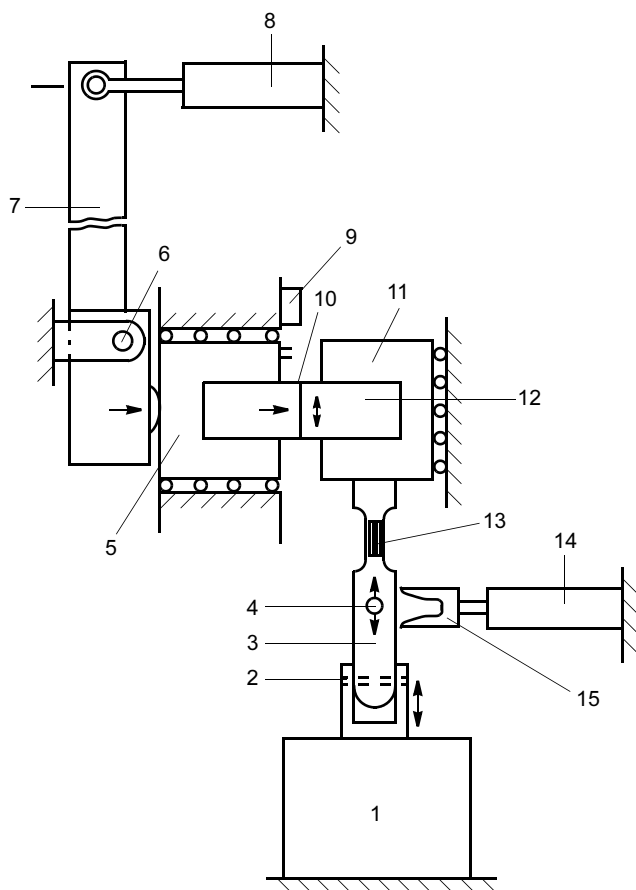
Схема экспериментальной установки для СЛТ [9]: 1 — генератор для испытания на усталость; 2 — штифт; 3 — тяга; 4 — установочный штифт; 5 — фиксатор (неподвижный); 6 — ось поворота; 7 — плечо рычага; 8 — пневматический узел для передачи фрикционного и ковочного давления; 9 — выключатель (предохранитель); 10 — стык; 11 — фиксатор (колеблющийся); 12 — стыкуемые образцы; 13 — тензометры; 14 — пневматический узел; 15 — установочная вилка
